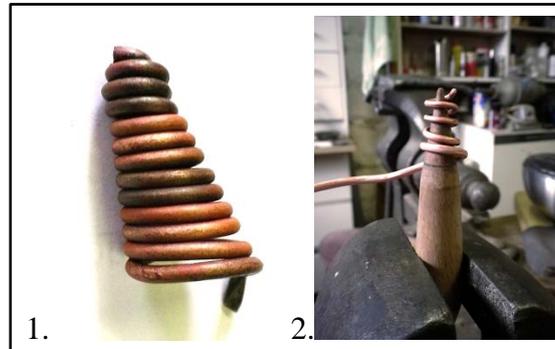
1. Enroulement à partir de la pointe, fil de section régulière : 2 mm.
